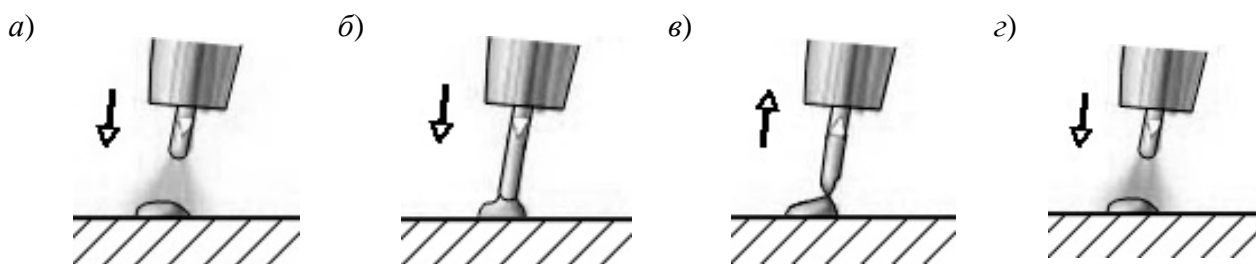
Установка для сварки плавлением с использованием технологии CMT
